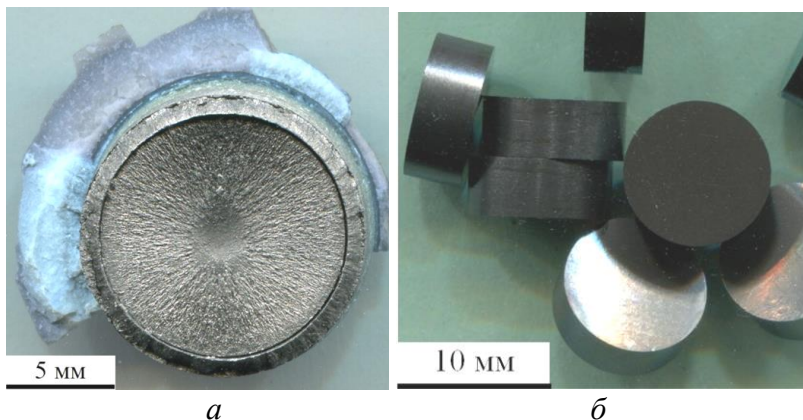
Композит сBN-LC(2): а – спечена заготовка в графітовому нагрівнику КВТ; б – вигляд змінних ріжучих пластини RNGN 09T300F з композиту для оснащення інструменту після алмазно-абразивної обробки заготовок
